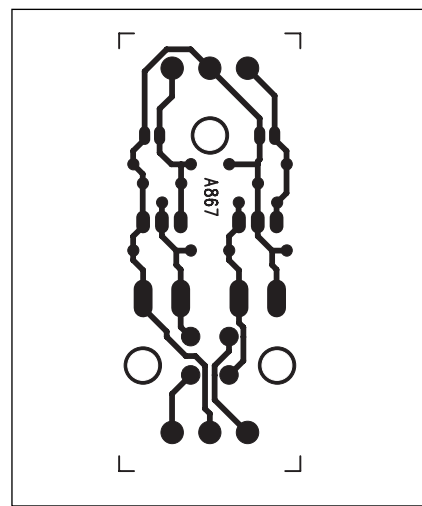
Obrazec desky spojů modulu (A99865)
